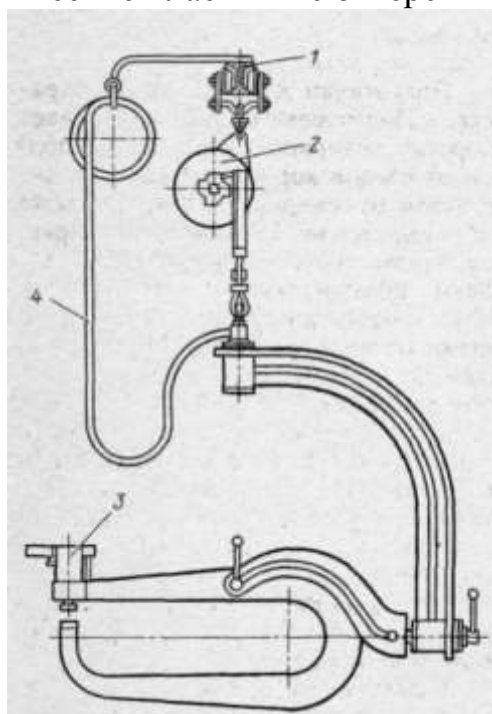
Скоба для рихтовки крыши кабины грузового автомобиля:
